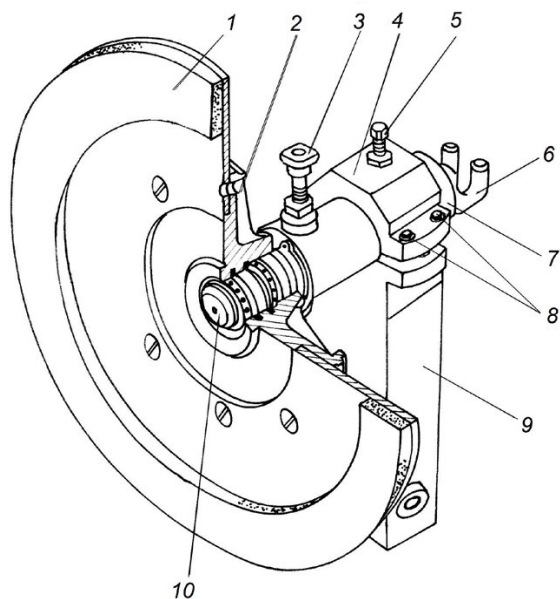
Заточное устройство: 1 – диск заточный; 2 – диск; 3 – стопор; 4 – корпус верхний; 5 – фиксатор; 6 – винт; 7 – корпус; 8 – болты; 9 – стойка; 10 – шток
